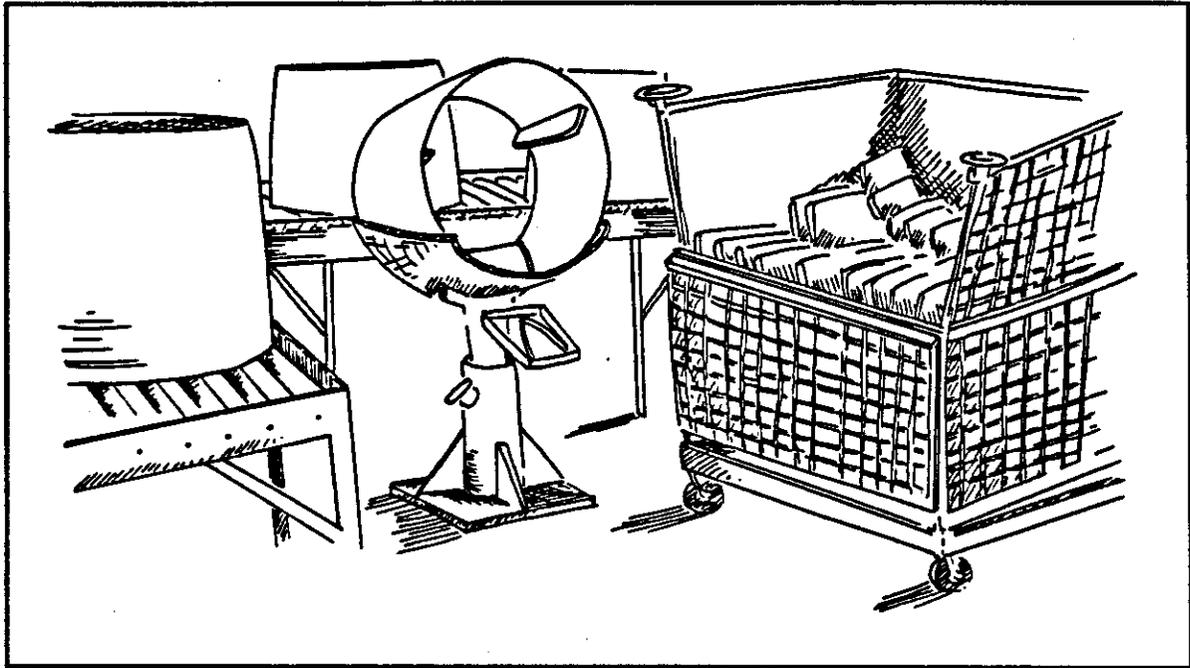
Poste d'insertion des ailettes, vue d'ensemble
